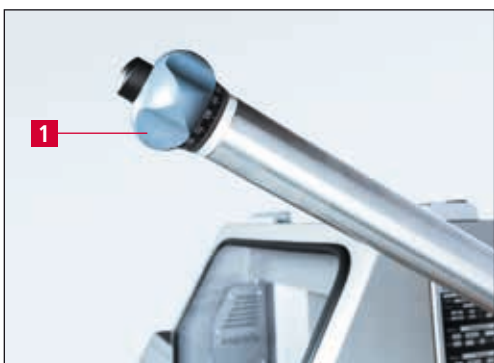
Рычаг управления «Шлифовальный блок»
